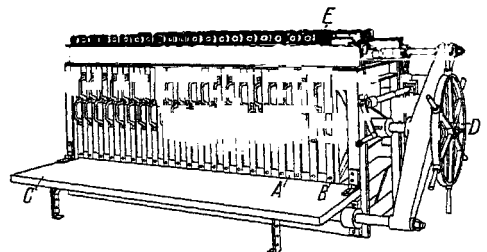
Kühlmaschine von HAUFF, Berlin. A Seifenrahmen; B Kühlkammer; C Plattform zum Ausziehen des Rahmens; D Handrad der Schraubenspindel; E Rollenführung der Kühlkammern.
